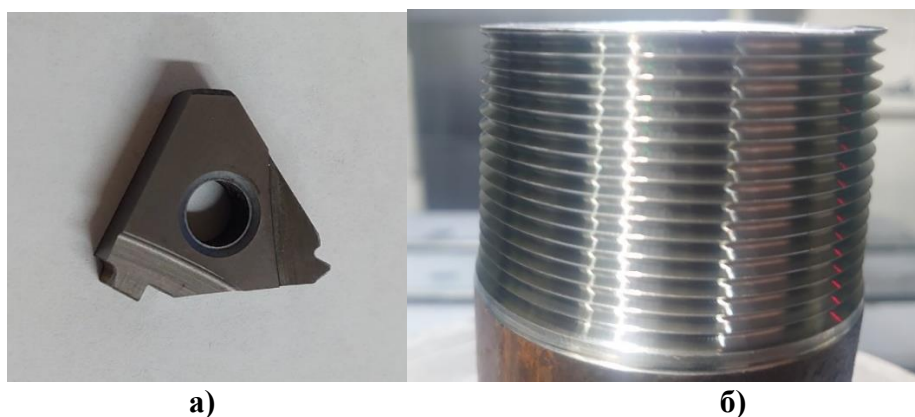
Резьбовая пластина а) конструкция пластины б) обработанная резьба
